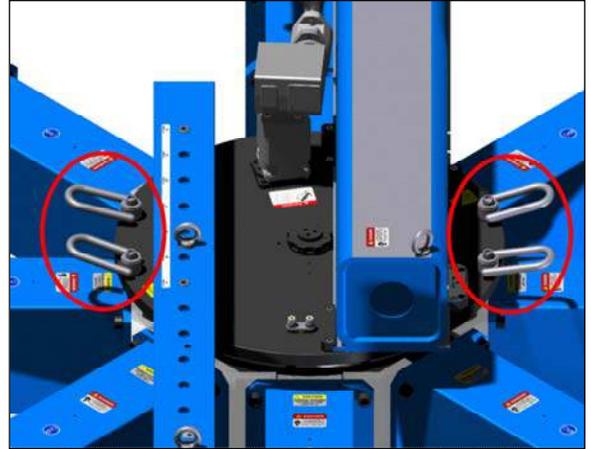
MESUREZ LA PIÈCE À TRAVAILLER
